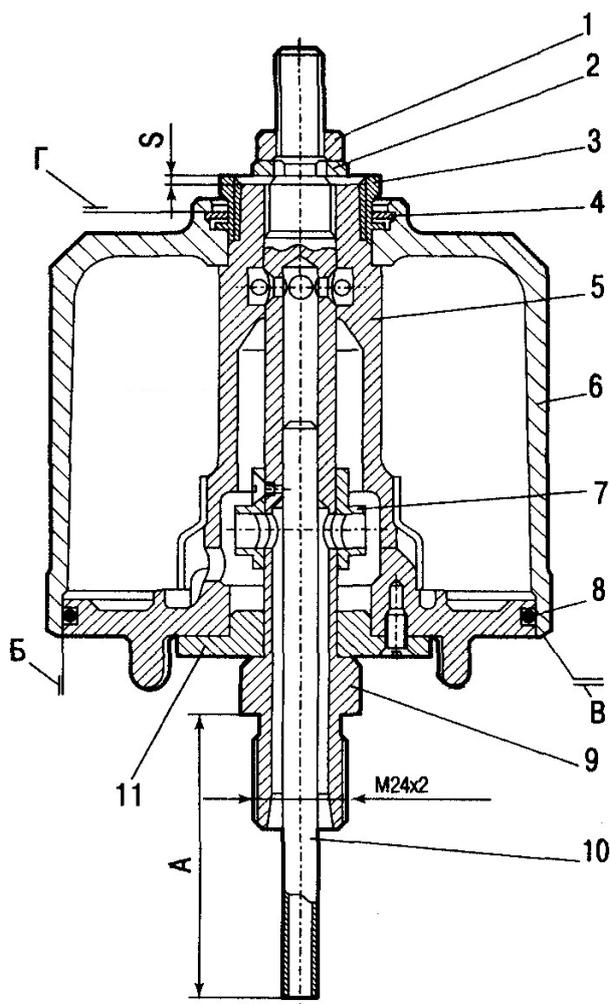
Ротор центробежного масляного фильтра в сборе с осью: 1 - гайка; 2 - упорная шайба; 3 - специальная гайка; 4 - упорное кольцо; 5 - корпус ротора; 6 - стакан ротора; 7 - насадка, 8 - уплотнительное кольцо; 9 - ось ротора; 10 - трубка; 11 - крышка корпуса ротора; Б, В, Г - поверхности; А, S - размеры
